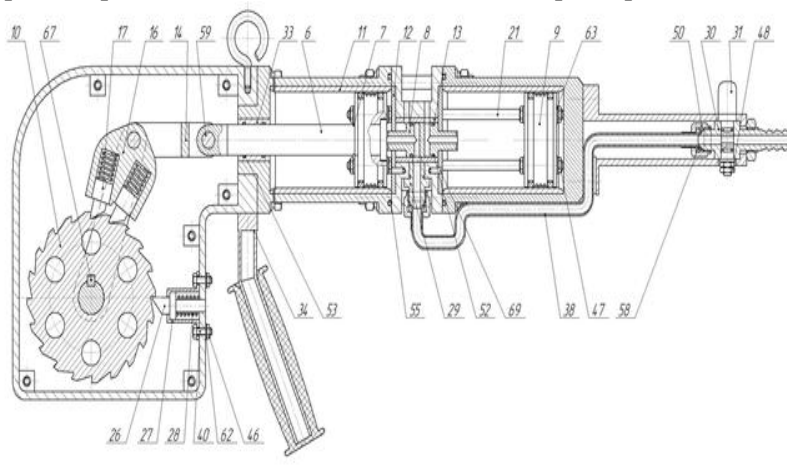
Схема пневматического гайковерта с кривошипом
